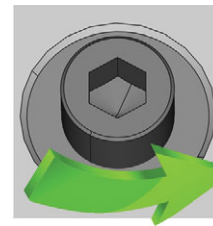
DIE SCHRAUBE AN DER GEWÜNSCHTEN POSITION LÖSEN
